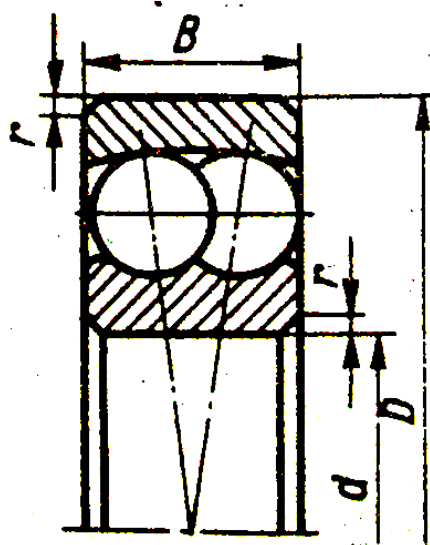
Подшипник шариковый радиальный сферический двухрядный (из ГОСТ 28428-90)
